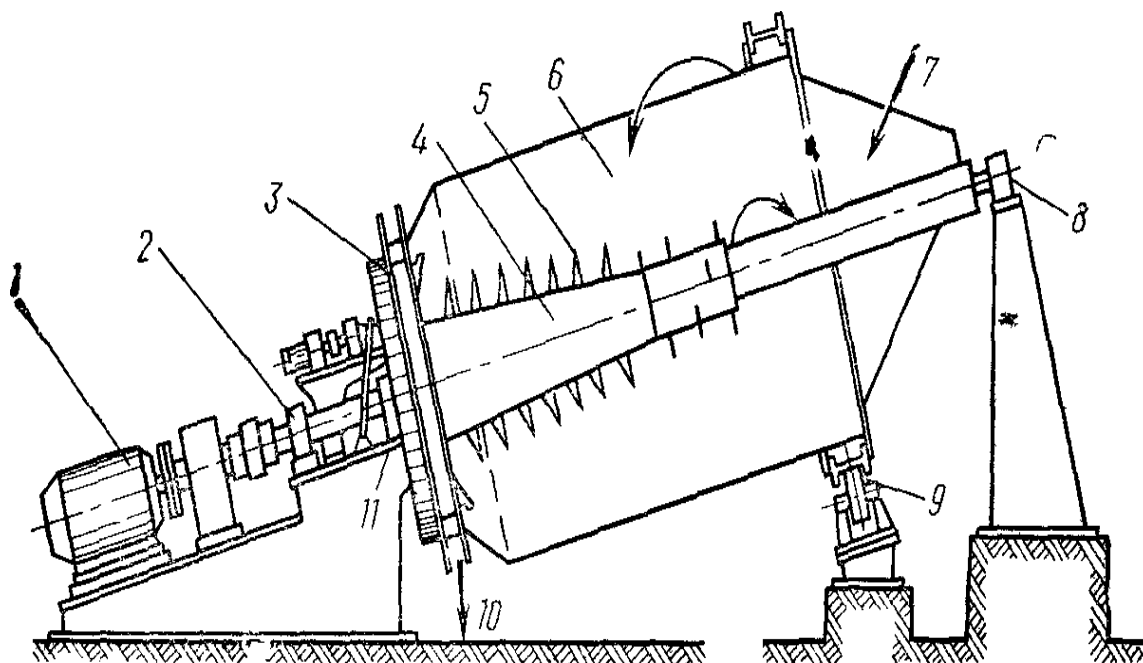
Гидроразбиватель макулатуры при высокой концентрации типа «Lamort-2000»: 1 - электродвигатель; 2, 8 - подшипниковая опора; 3 - диск; 4 - ротор; 5 - зубья; 6- ванна; 7- воронка; 9- ролик; 10- патрубок
